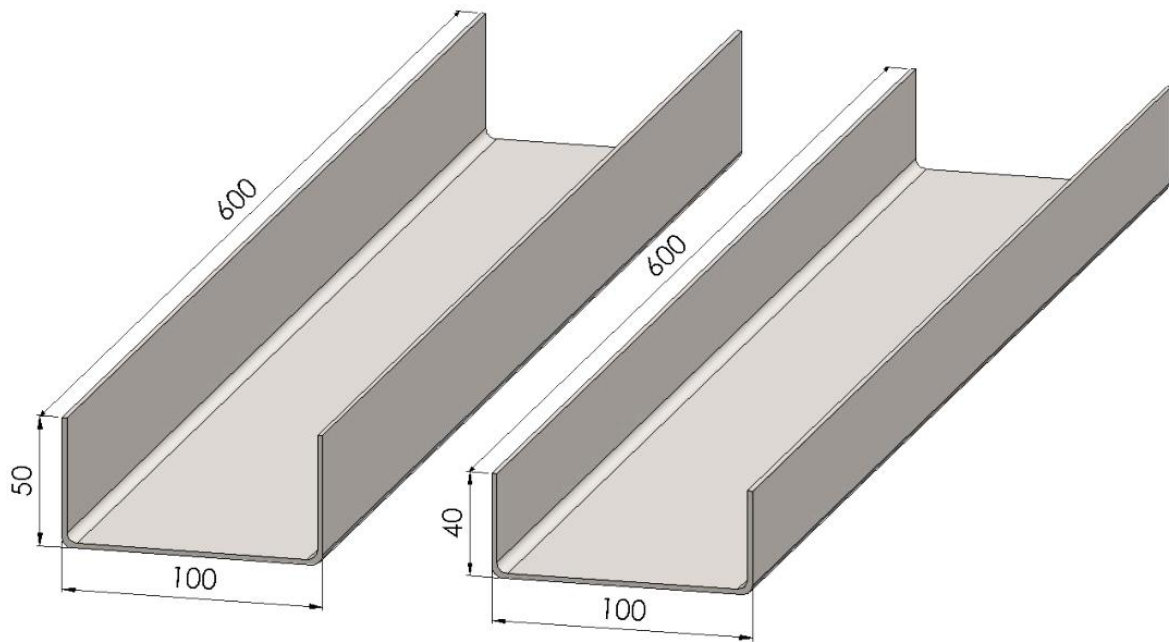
Dimensões em (mm) das seções transversais dos perfis U
